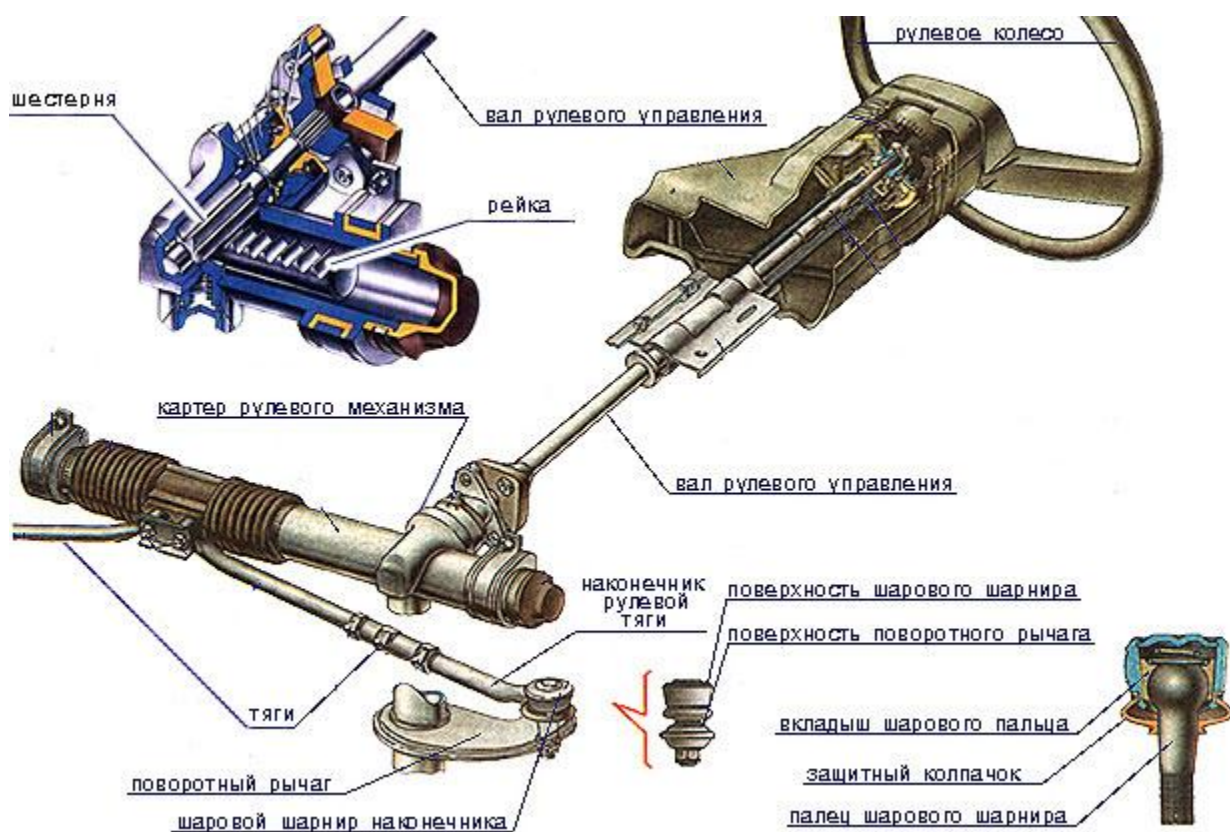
Рулевой механизм типа шестерня-рейка
